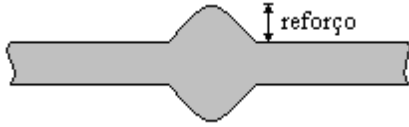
Perfil do material que compõe o tanque de armazenamento com solda.
